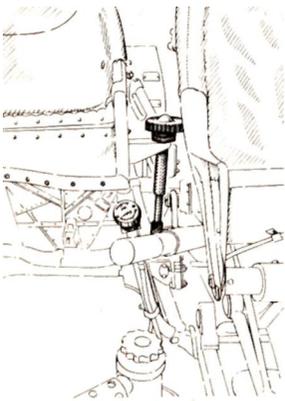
Hilfssteuerung für Seitenrudder (gegen Flugrichtung)
